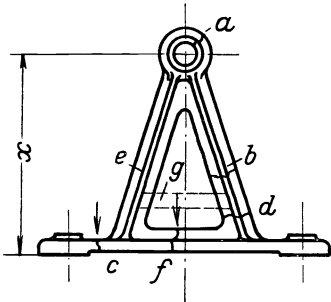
Autogene Schweißungen an einem Lagerbock.
